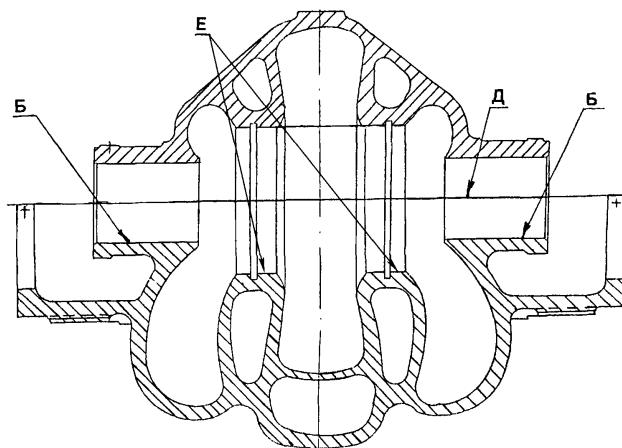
Корпус, крышка насоса СЭ 2500–60–11 (рисунок 10, поз.
